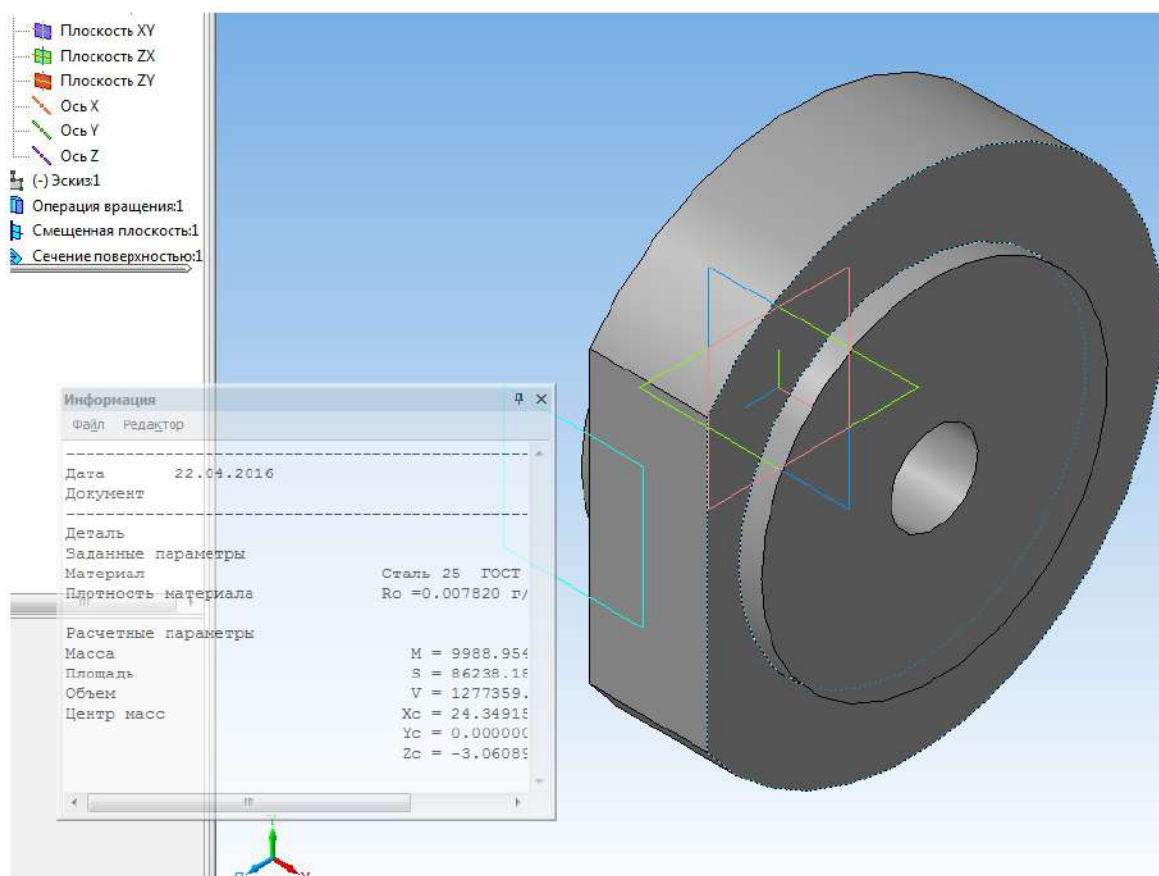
Виготовлення заготовки відцентровим литтям
